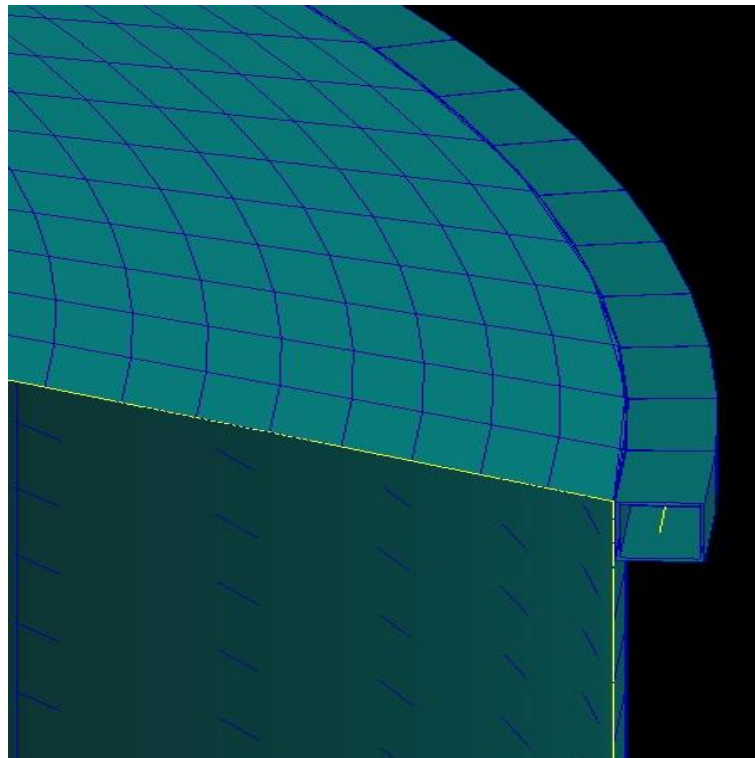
Skica odabranih dimenzija za plašt cilindra
